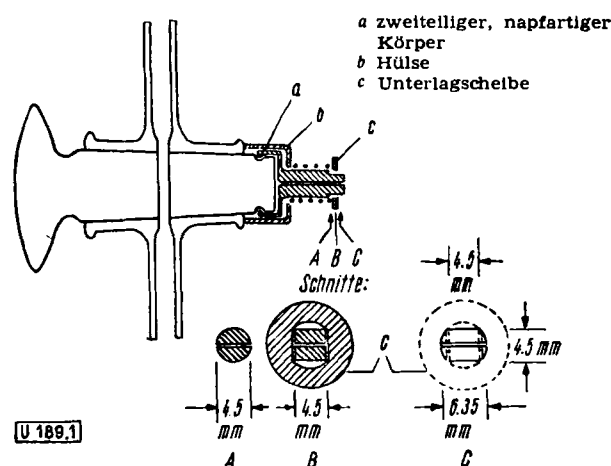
Vorrichtung zur Umwandlung gewöhnlicher Glasschliff-Hähne in Druckhähne.
